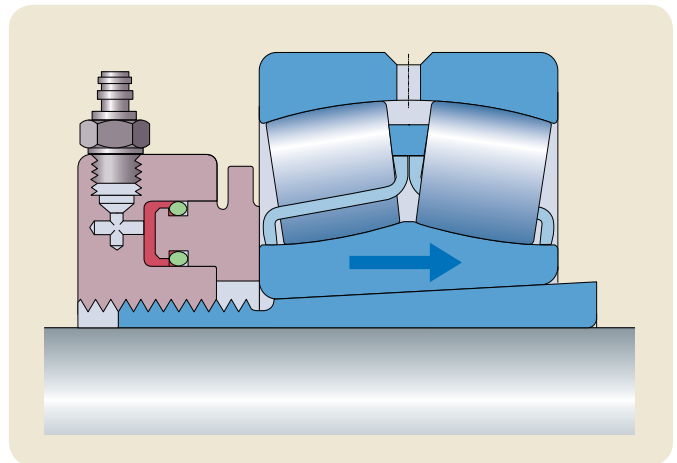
Roulement monté sur un manchon de serrage et poussé.
